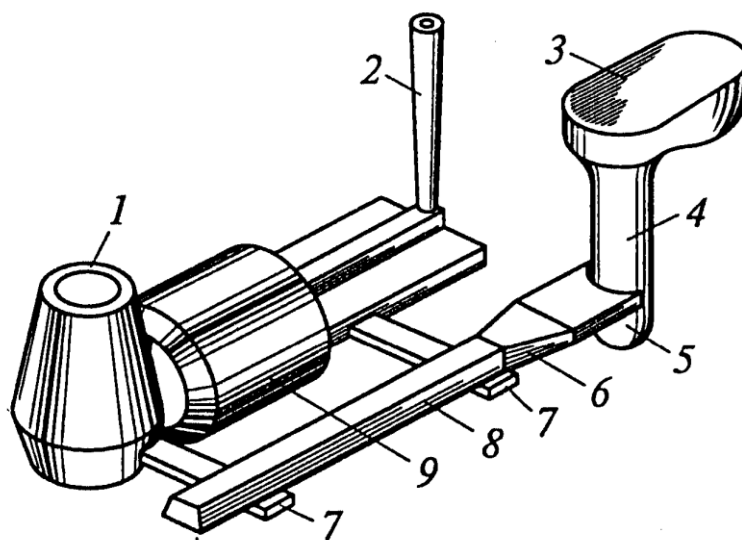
Общий вид литниковой системы: 1 – прибыль; 2 – выпор; 3 – литниковая чаша; 4 – стояк; 5 – зумпф; 6 – литниковый дроссель; 7 – питатели; 8 – шлакоуловитель; 9 – отливка
